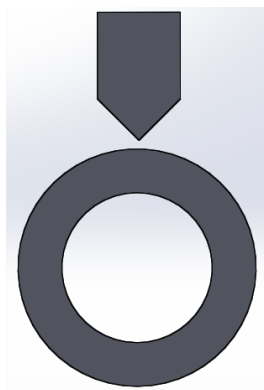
Seção transversal da junta a ser soldada entre tubo e barbatana do MCV
